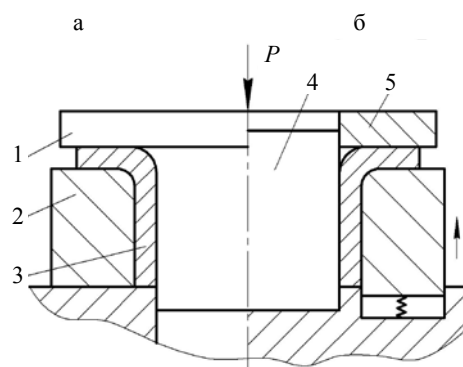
Схемы: а – раздачи; б – осадки трубной заготовки; 1 – пуансон; 2 – матрица; 3 – заготовка; 4 – цилиндрический стержень; 5 – пресс-шайба
